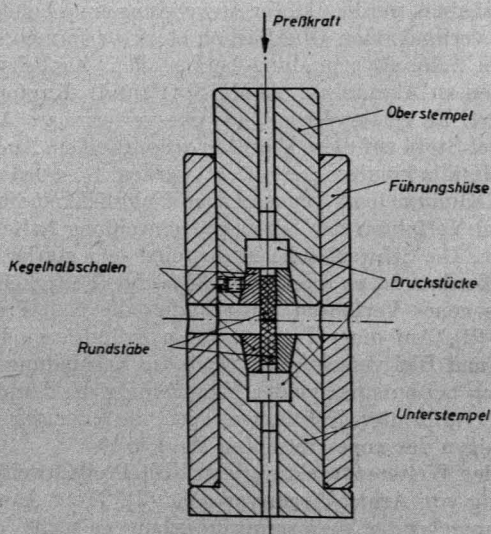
Vorrichtung zum Kalt-Preßschweißen
